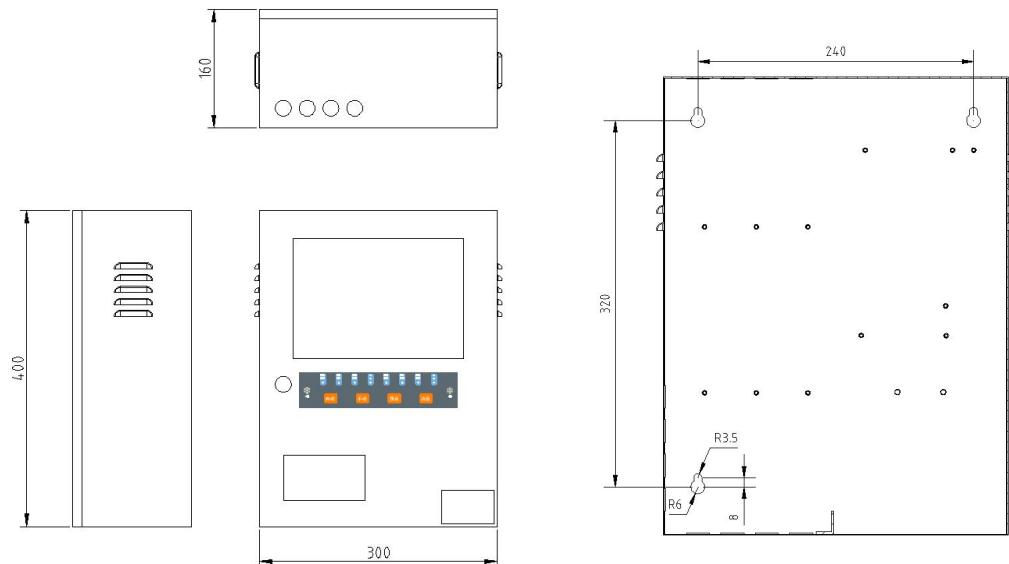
A-C-A100/B3 型应急照明控制器外形尺寸图和安装尺寸图
